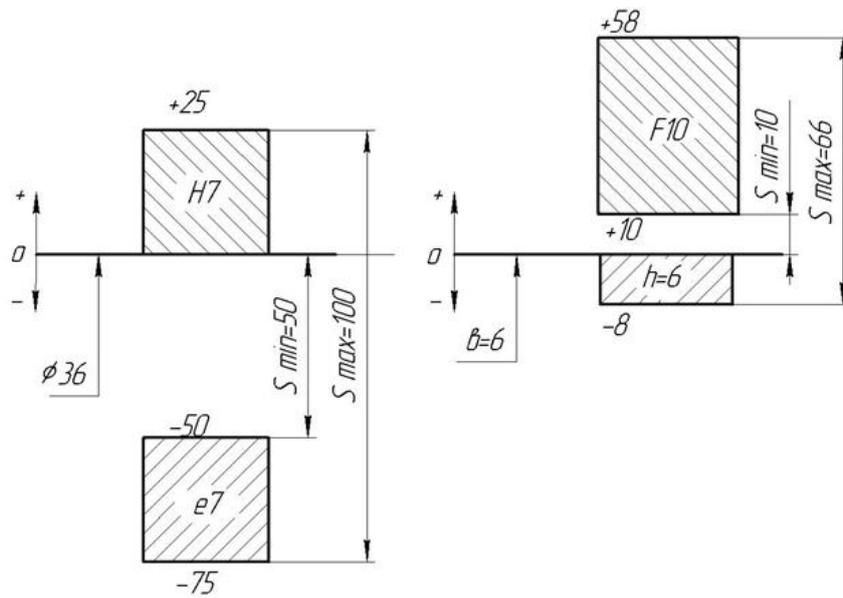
Схеми розташування полів допусків посадок шліцевого з'єднання
